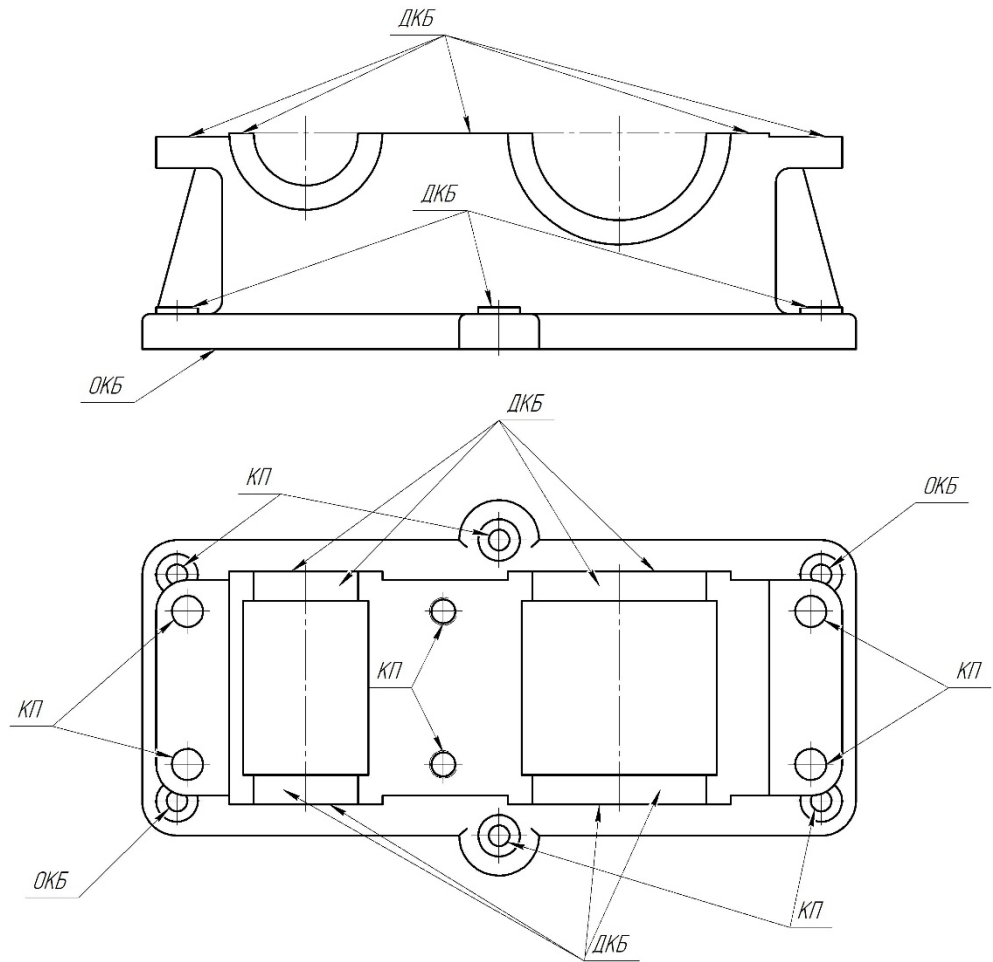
Класифікація поверхонь деталі «Корпус редуктора».
